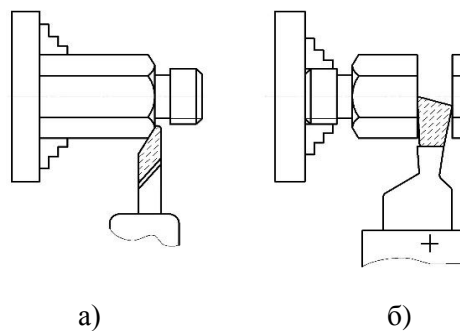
Обточування фаски на шестиграннику та переустановлення заготовки
